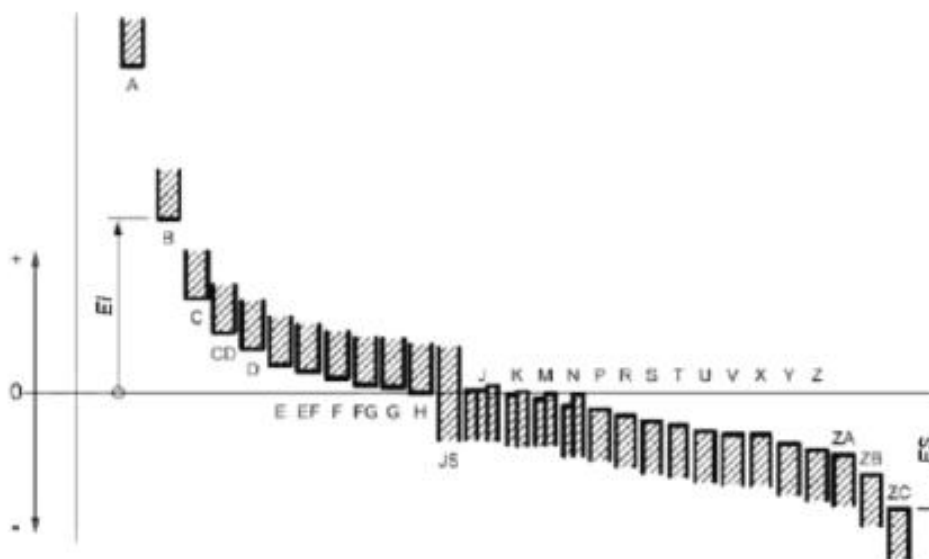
Расположения интервалов допуска относительно номинального размера для основных отклонений отверстий
